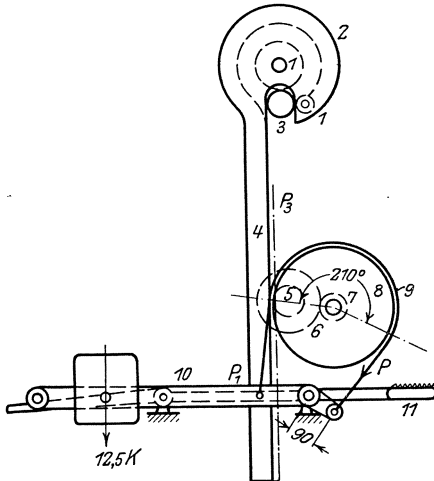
Wickelvorrichtung für Schlagmaschinen.
